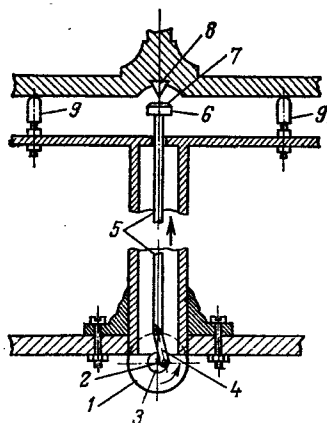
Схема подъемного механизма арретирующего приспособления:
